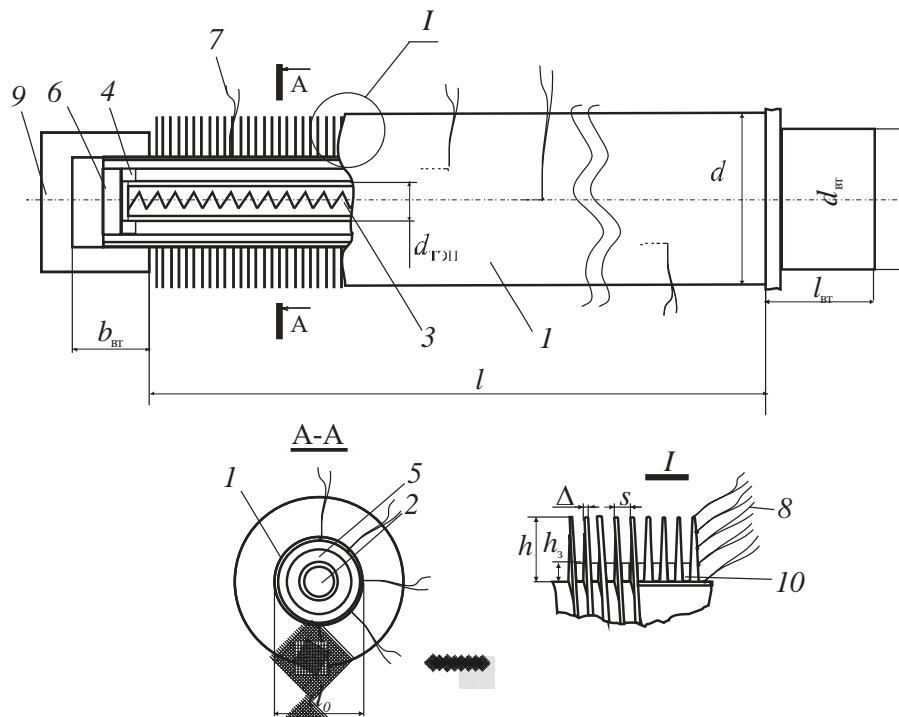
Общий вид calorиметрической трубы: 1 – биметаллическая ребристая труба; 2 – трубчатый электронагреватель (ТЭН); 3 – спираль ТЭНа; 4 – центровочное кольцо; 5 – кварцевый песок; 6 – высокотемпературная силиконовая замазка; 7 – медь-константановые термопары у основания ребер; 8 – медь-константановые термопары по высоте ребра; 9 – фторопластовая втулка; 10 – льняной шнур
